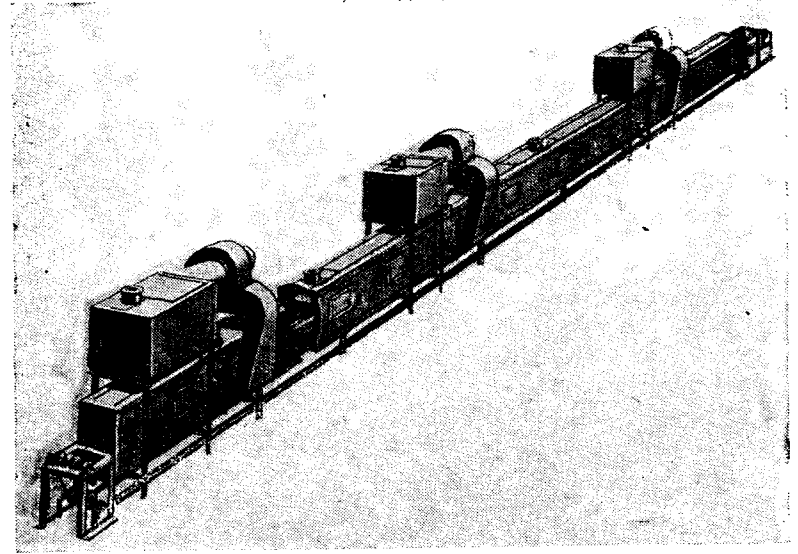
Внешний вид конвейерного туннельного сушила для сушки свеженамазанных пластин с камерой квадратного сечения и распределительными каналами по зонам
